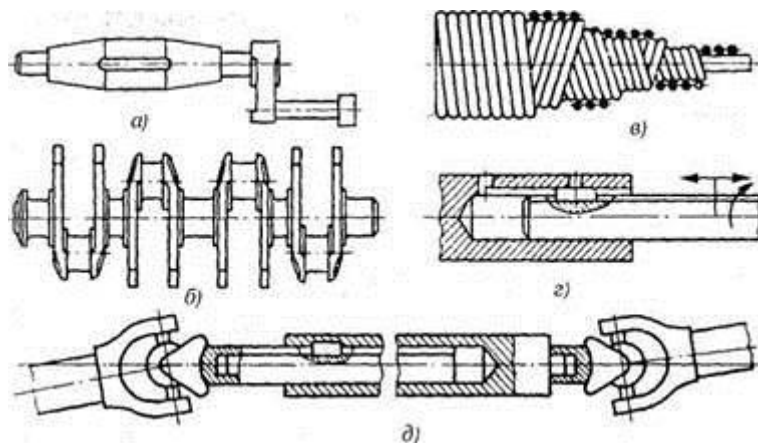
Типы валов: а — кривошипный вал; б — коленчатый вал; в — гибкий вал;
